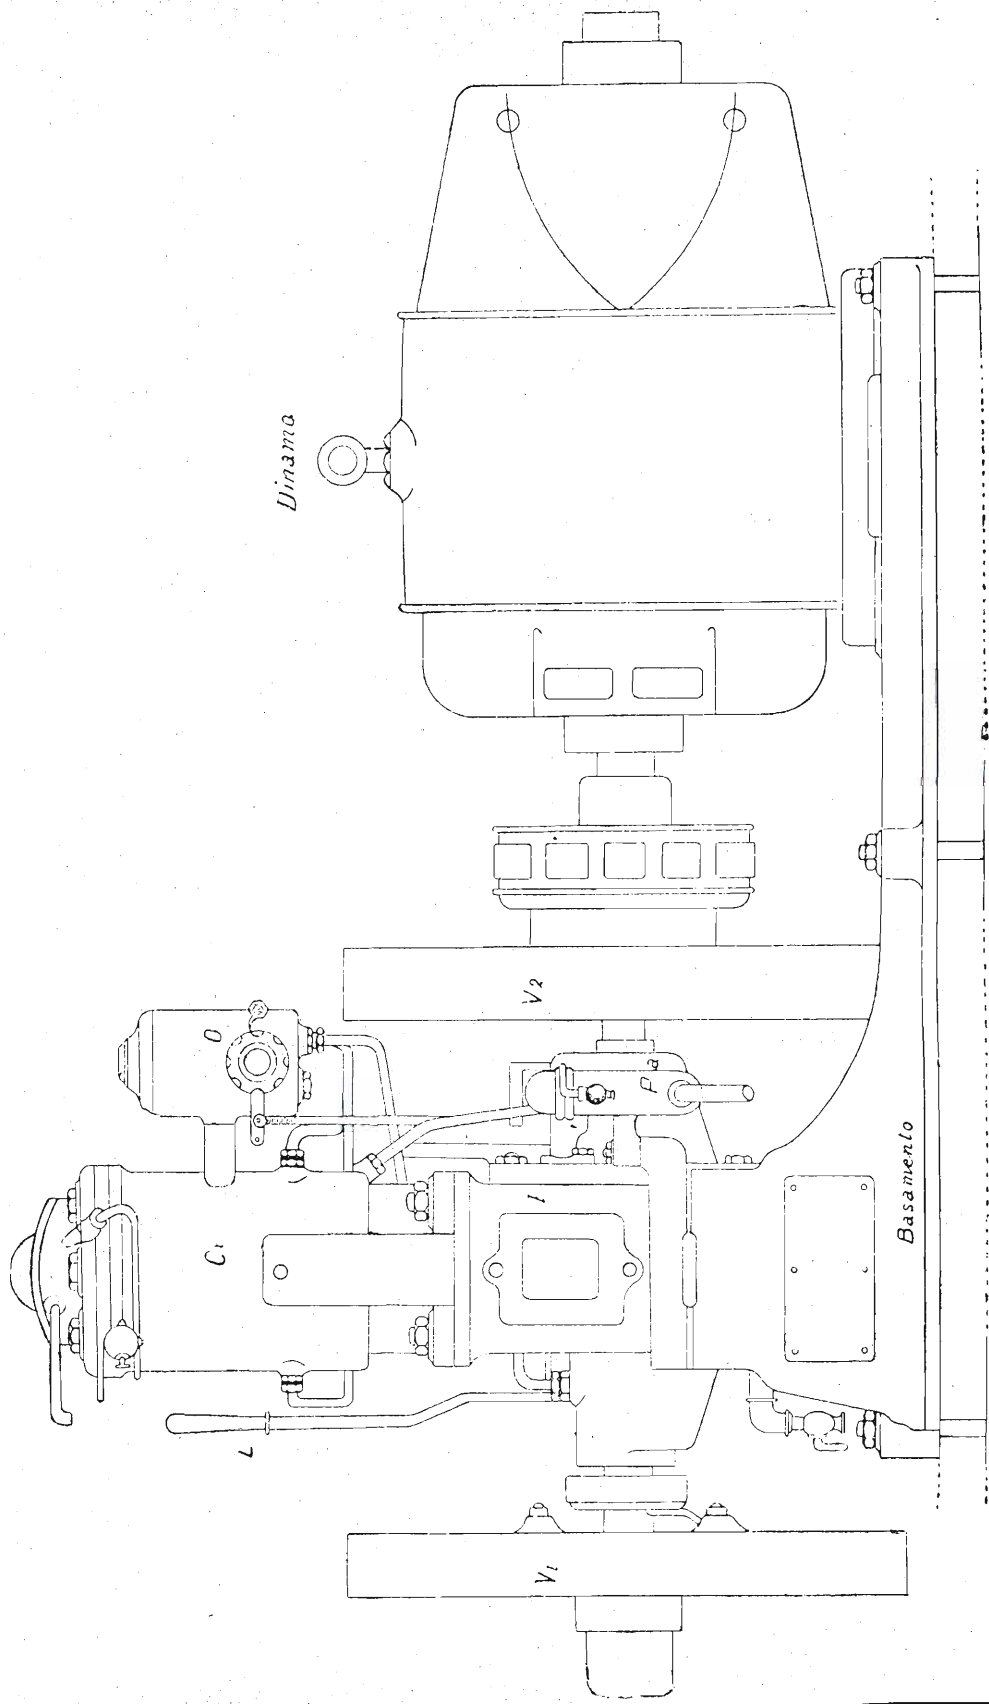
Complesso elettrogeneratore con motore a testa calda tipo Muzzi
